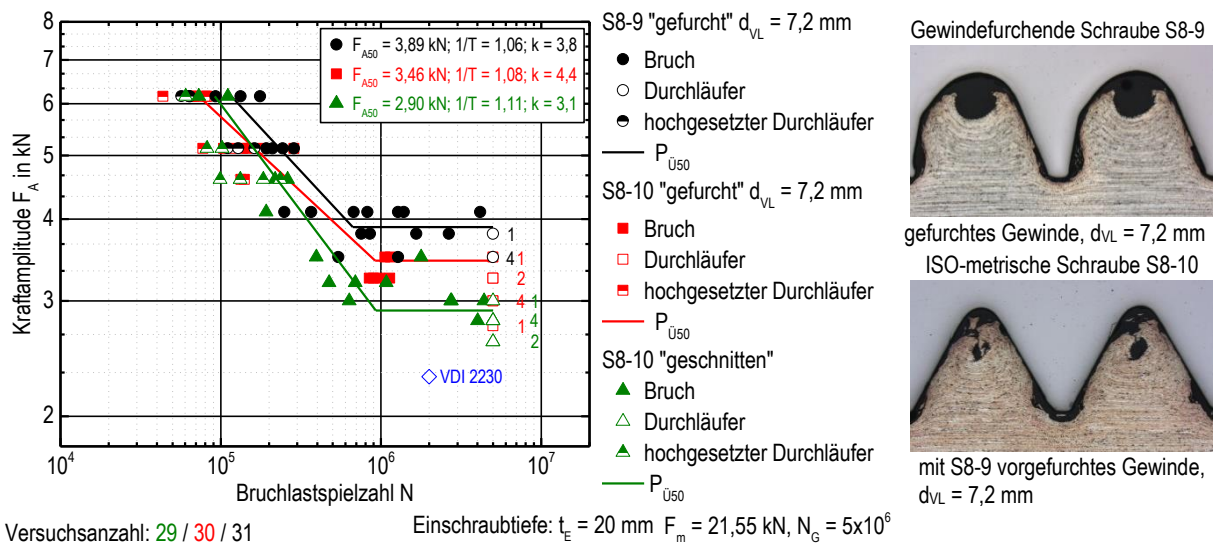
Bauteilwöhlerlinien ermittelt im axialen Schwingversuch für die gewindefurchende Schraube S8-9 und die ISO-metrische Schraube S8-10 in gefurchtem und geschnittenem Mutterngewinde. Für gefurchte Gewinde: Vorlochdurchmesser $d_{VL} = 7,2$ mm. nach [88, 89]
